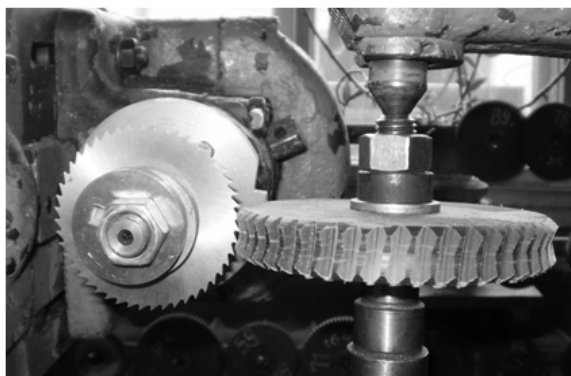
Нарізання глобоїдного черв'ячного колеса дисковою фрезою на зубофрезерному верстаті. Кількість зубців: колеса – $z_k=50$; фрези – $z_f=48$; матеріал колеса – текстоліт, зовнішній діаметр – $D_a=132$ мм
